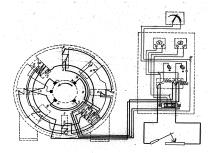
Схема соединений сварочного генератора типа СГП-3-VIII; вид со стороны коллектора
